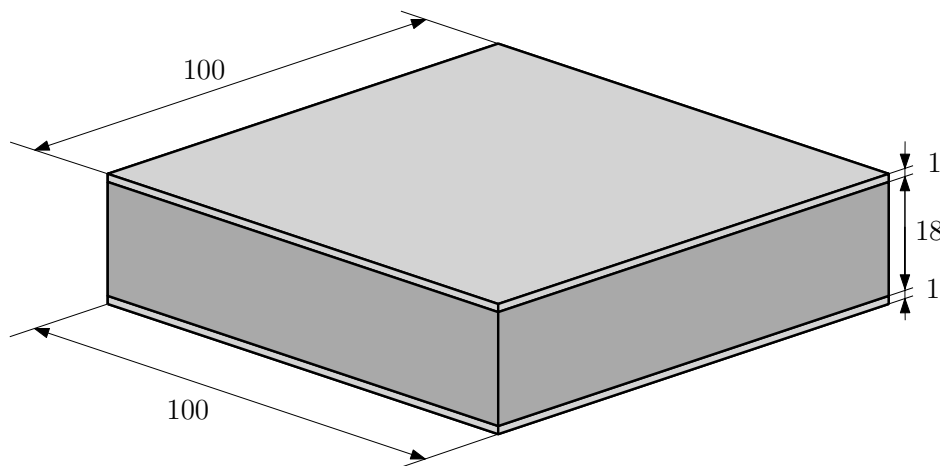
Desenho com as dimensões dos provetes utilizados nos testes de impacto em torre de queda.
